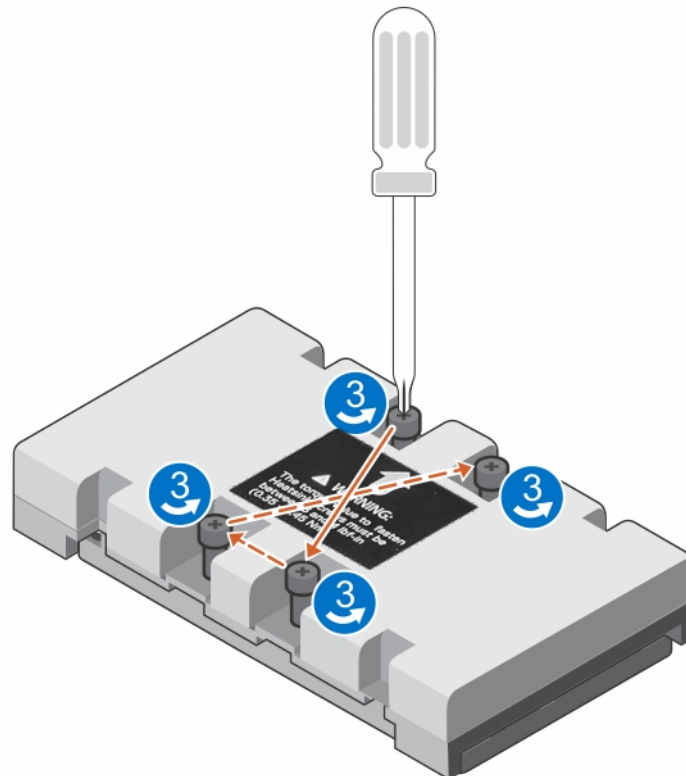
Entfernen der SXM2-GPU-Kühlkörperschrauben
